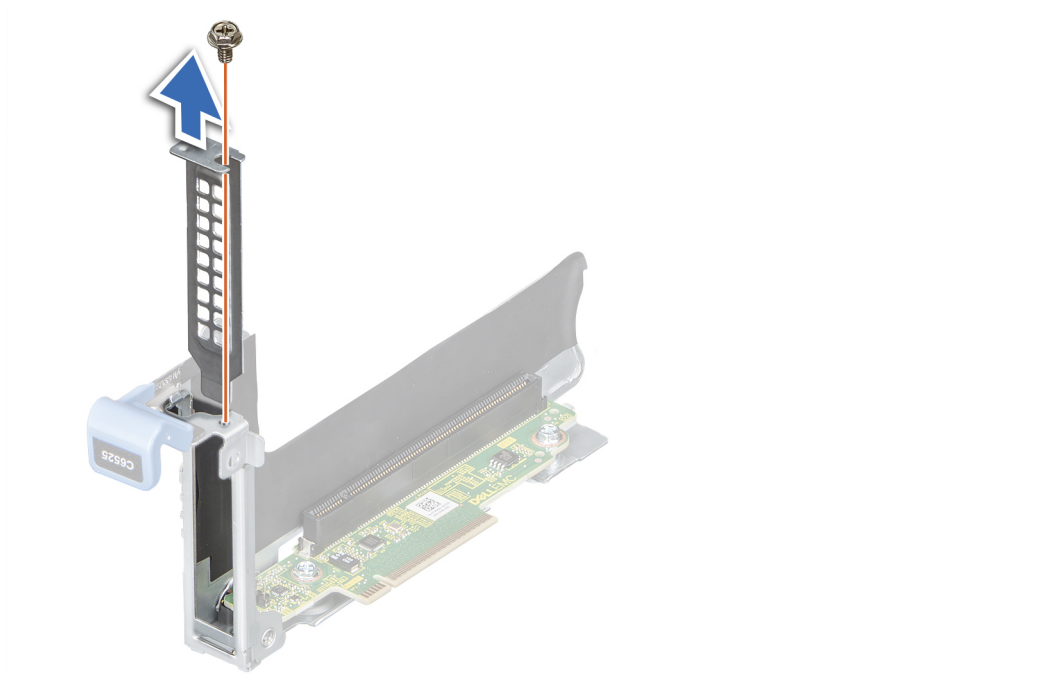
Retrait du support de la plaque de recouvrement de carte d'extension
